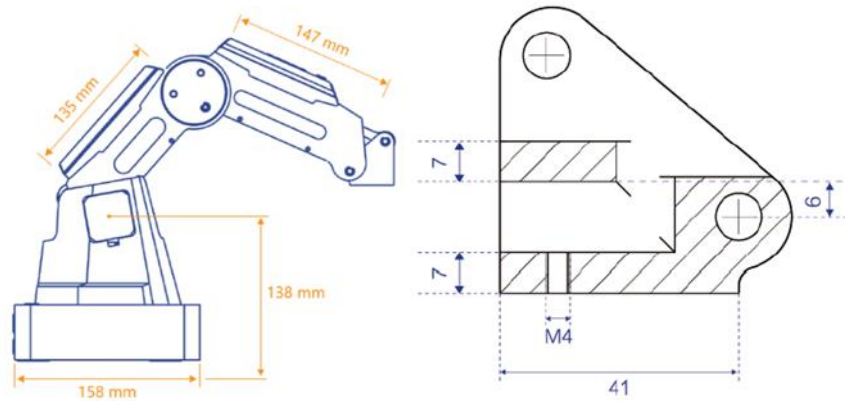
dimensions du bras du robot et du dispositif de fixation des outils.
